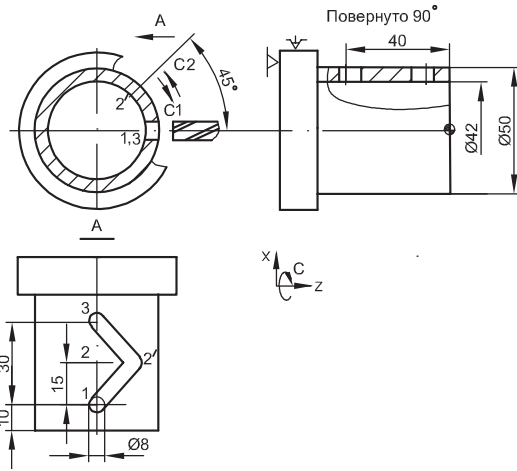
Циліндрична інтерполяція. Фрезерування ламаного паза
